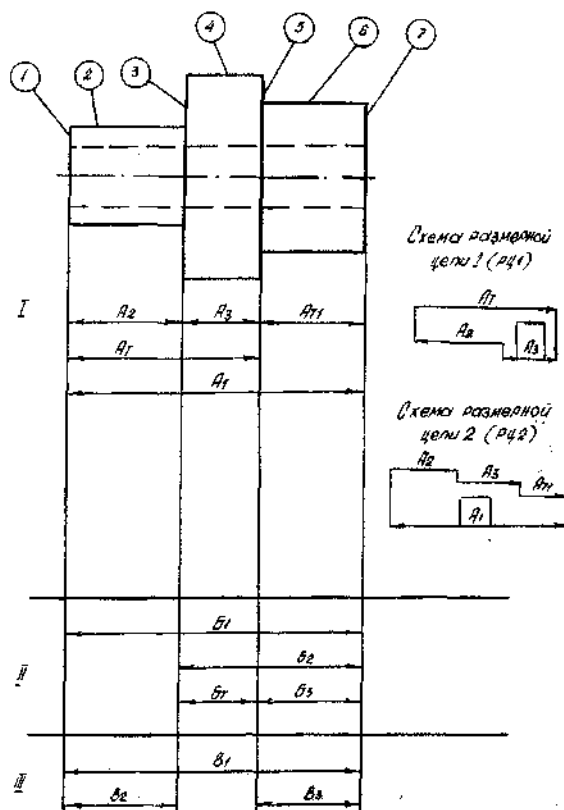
Варианты расстановки размеров в деталях типа втулки, фланцы, крышки; I, II, III-номера вариантов; 1, 2, 3, ..., 7-обрабатываемые поверхности; А, В с различными индексами-размеры, представленные на чертеже;  $A_{11}$ ,  $B_1$ -технологические размеры
